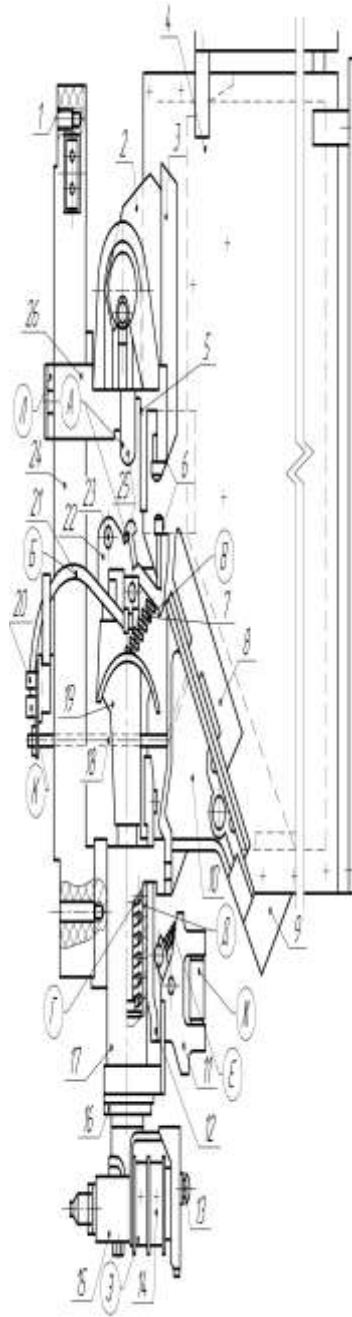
Лінійний контактор типу 1КП-005:
